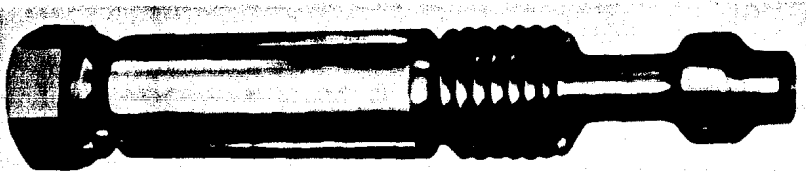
Pieza maquinada con el dispositivo de torneado longitudinal.
